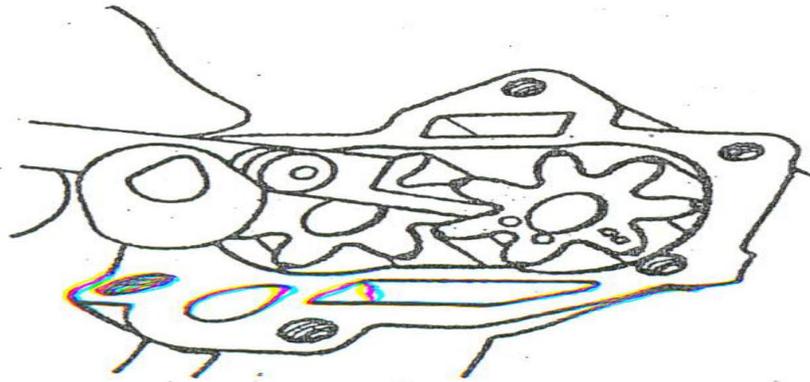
Verificación de tolerancias entre engranes y engrane con el calibrador
